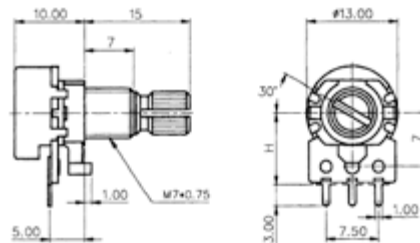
Габаритні розміри змінного резистора 16K1
